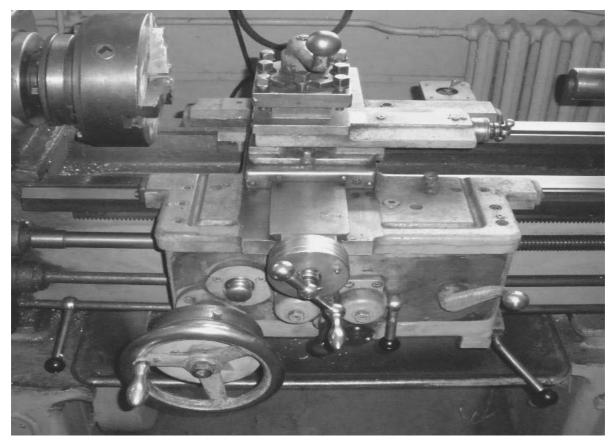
Суппорт токарно-винторезного станка модели 1А616П
